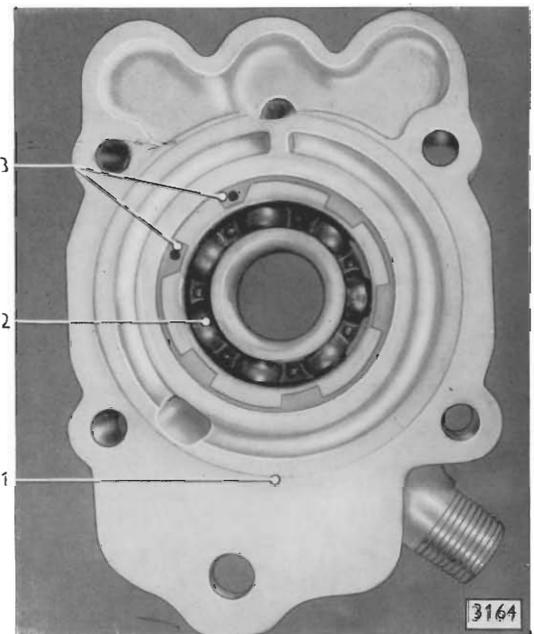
Kugellager in Getriebegehäuseendstück eingebaut
